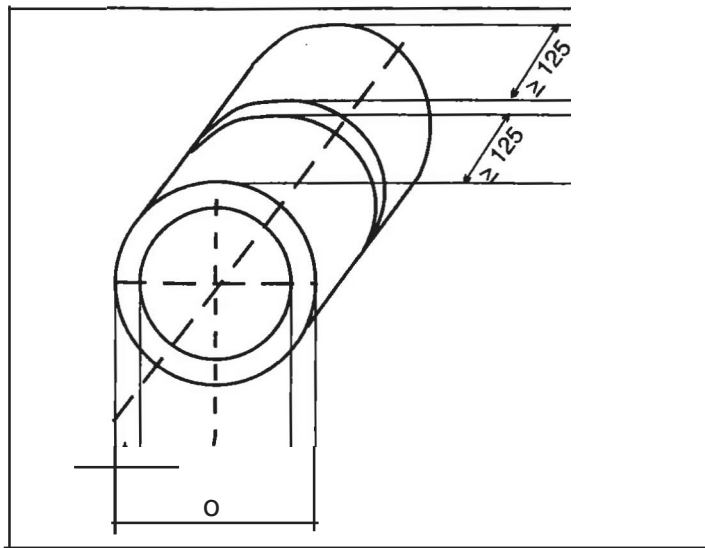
DIMENSIONES DEL CUPÓN DE PRUEBA PARA EL SOLDEO DE TUBOS A TOPE (DIMENSIONES EN MILÍMETROS)
